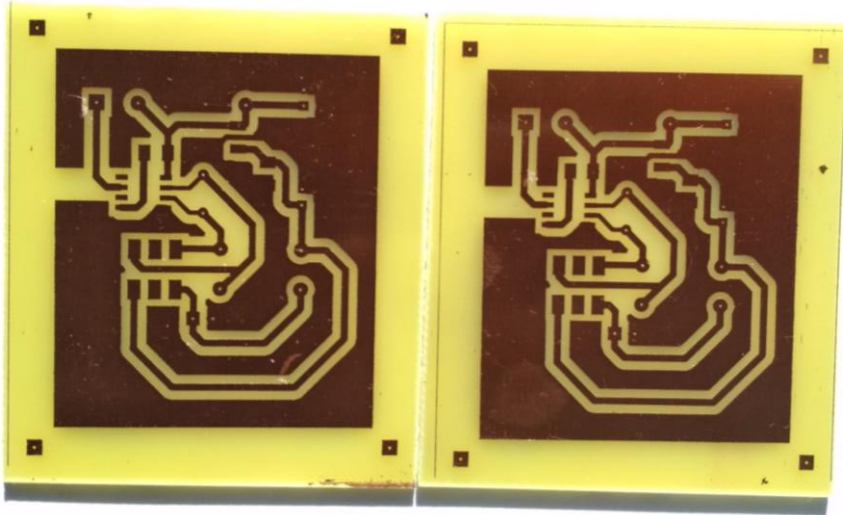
Resultado del revelado de la PCB del Receptor.
